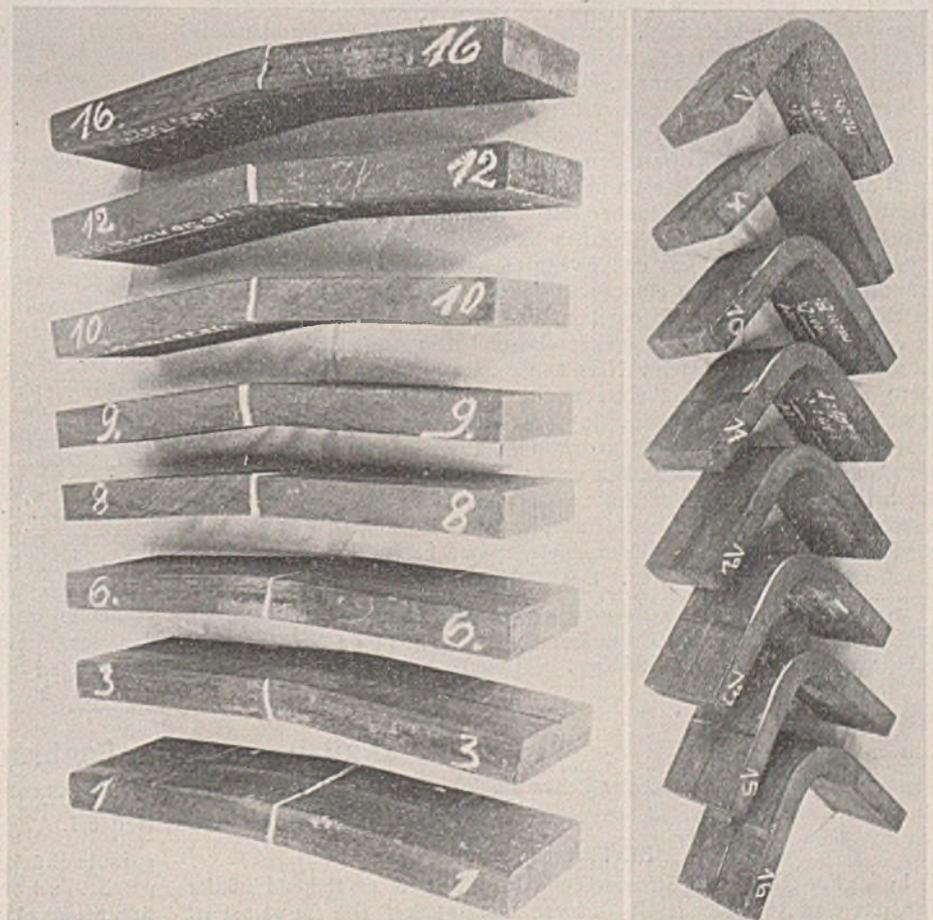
Schweißraupenbiegeprobe St 52, 55 mm dick. Prüfort: Reichsbahn-Zentralamt, Berlin.
